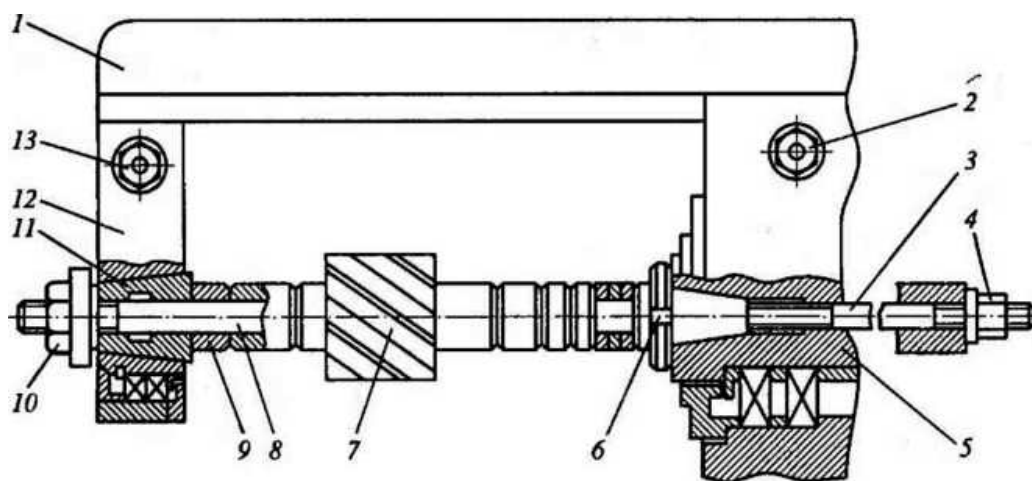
Оправка для установки цилиндрических и дисковых фрез:
